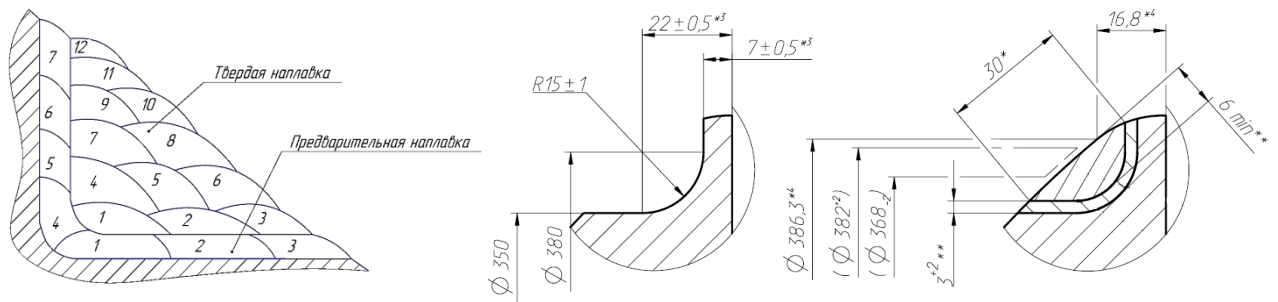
Неравномерная толщина наплавки и твердость поверхностного слоя
